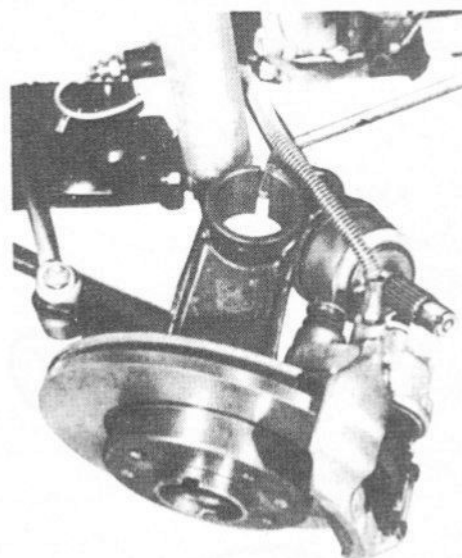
Débranchement de l'arbre de roue du moyeu (Sec 3)
